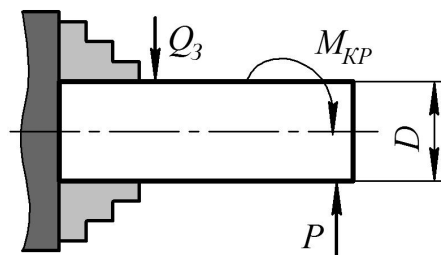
Схема різання для визначення сили закріплення для операцій точіння
